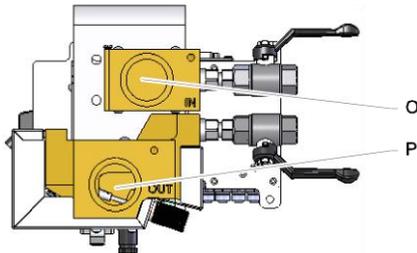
Соединительные разъемы конструкции "автономный прибор"
